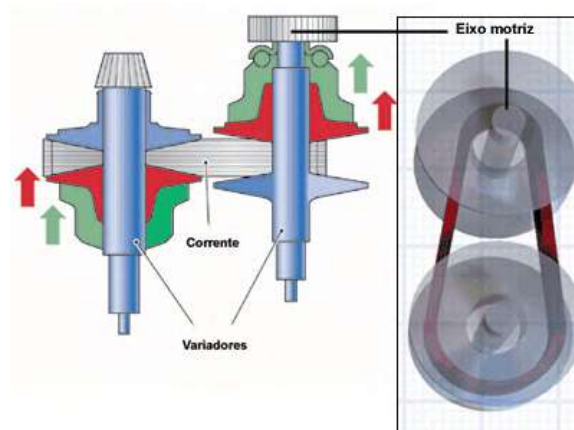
Corrente de elos de placa e engrenagens cônicas
